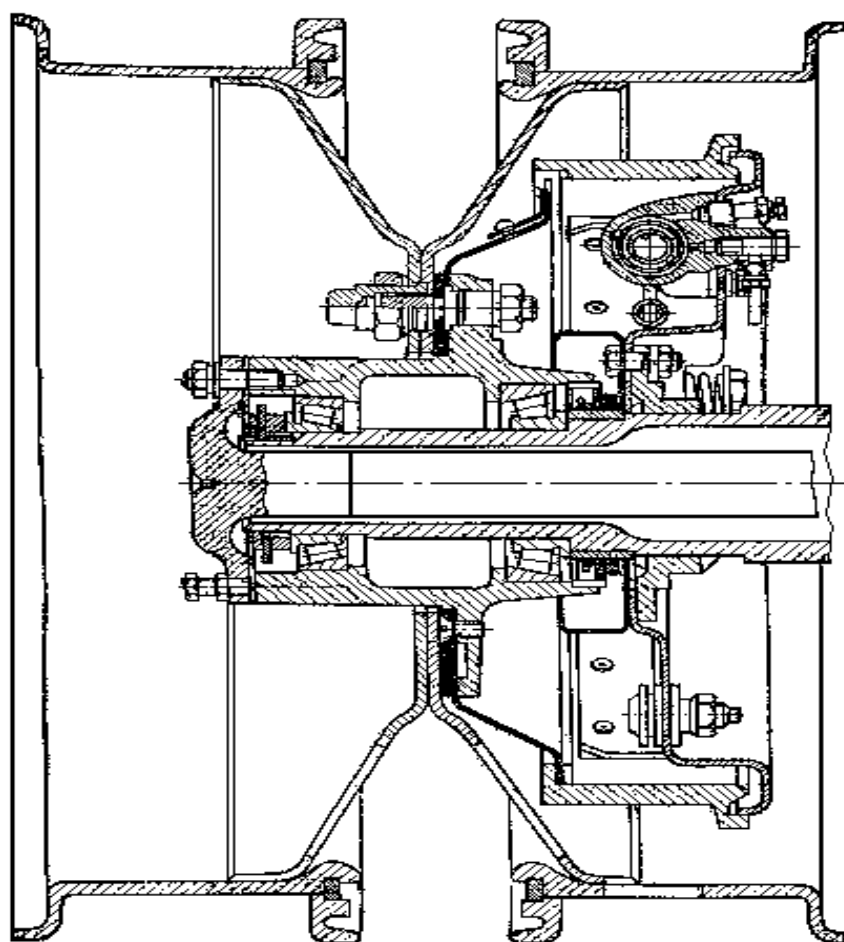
Ступица и обод ведущего колеса грузовика
